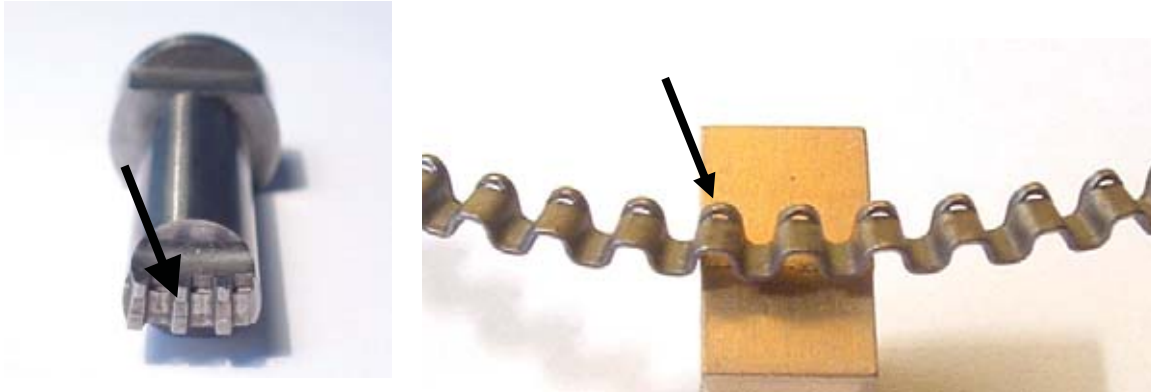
Urządzenie do tłoczenia elementów sprężystych typu Hastings
